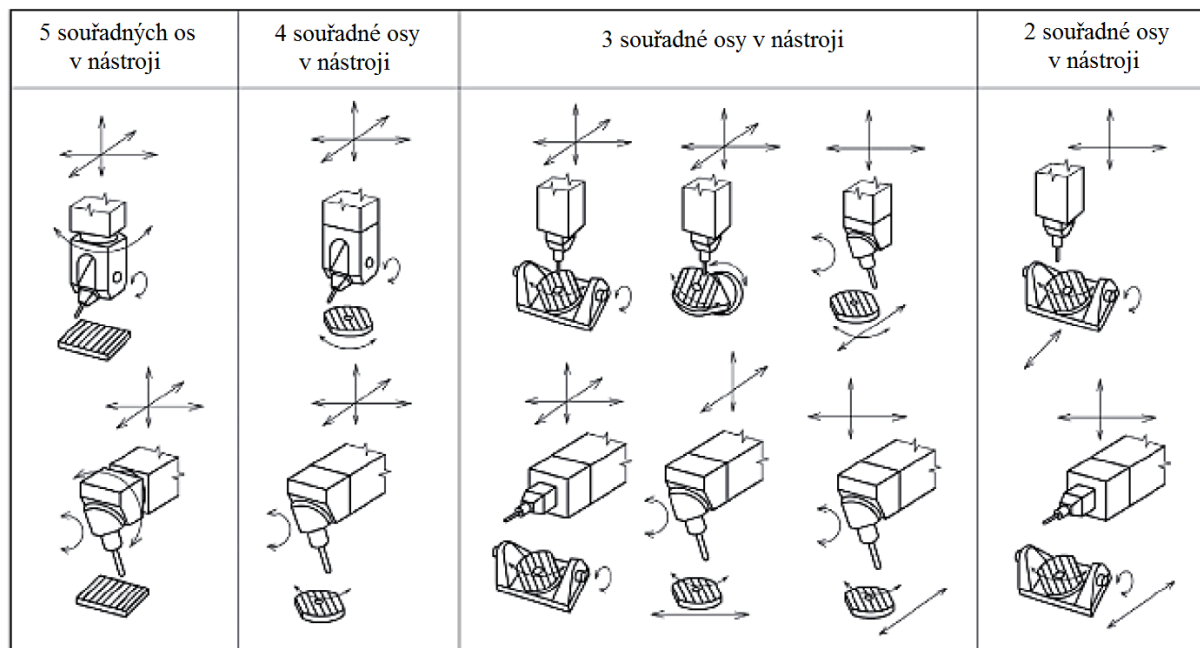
Rozdělení CNC obráběcích center na nerotační součásti [1]
